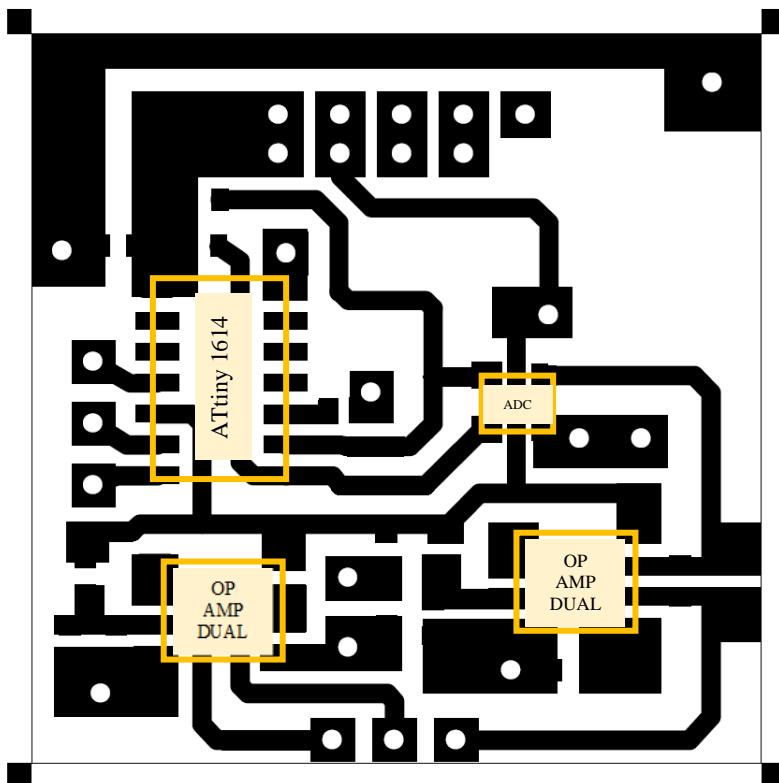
Disseny de la capa superior de la PCB que conté l'ATtiny marcant en groc els diferents dispositius que hi van soldats (sense considerar resistències ni condensadors).
